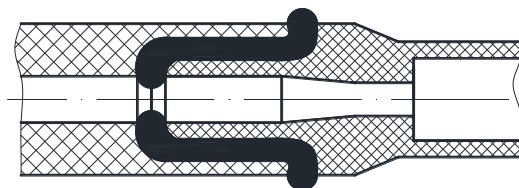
Конструктивные элементы шва сварного соединения (шов НС5)
